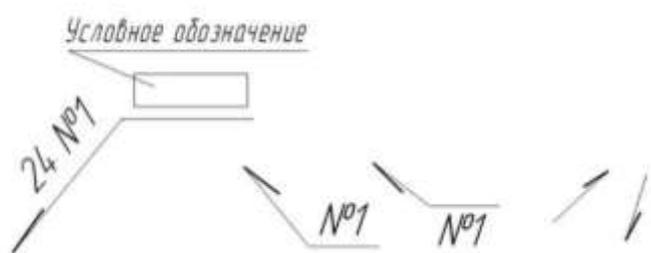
Условные обозначения при наличии на чертеже одинаковых швов:
